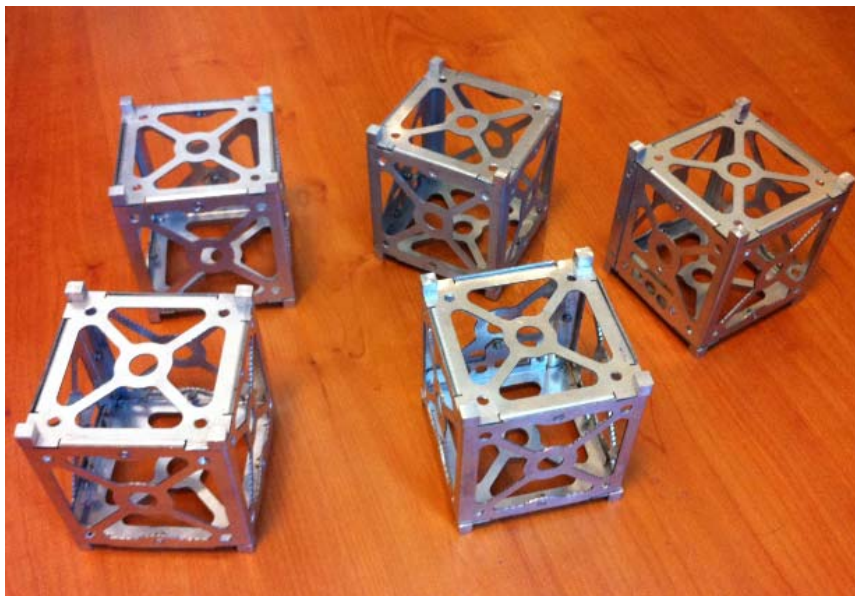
Construcción de los 5 prototipos estructurales tipo CubeSat terminados.
